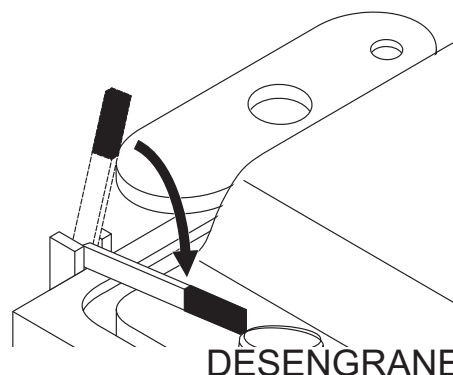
Palanca de transmisión de engrane/desengrane (posición de desengrane)
